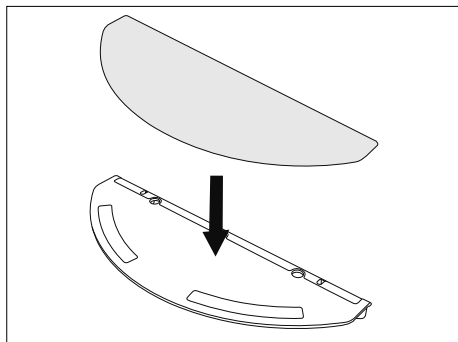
Montaggio dell'accessorio lavapavimenti
